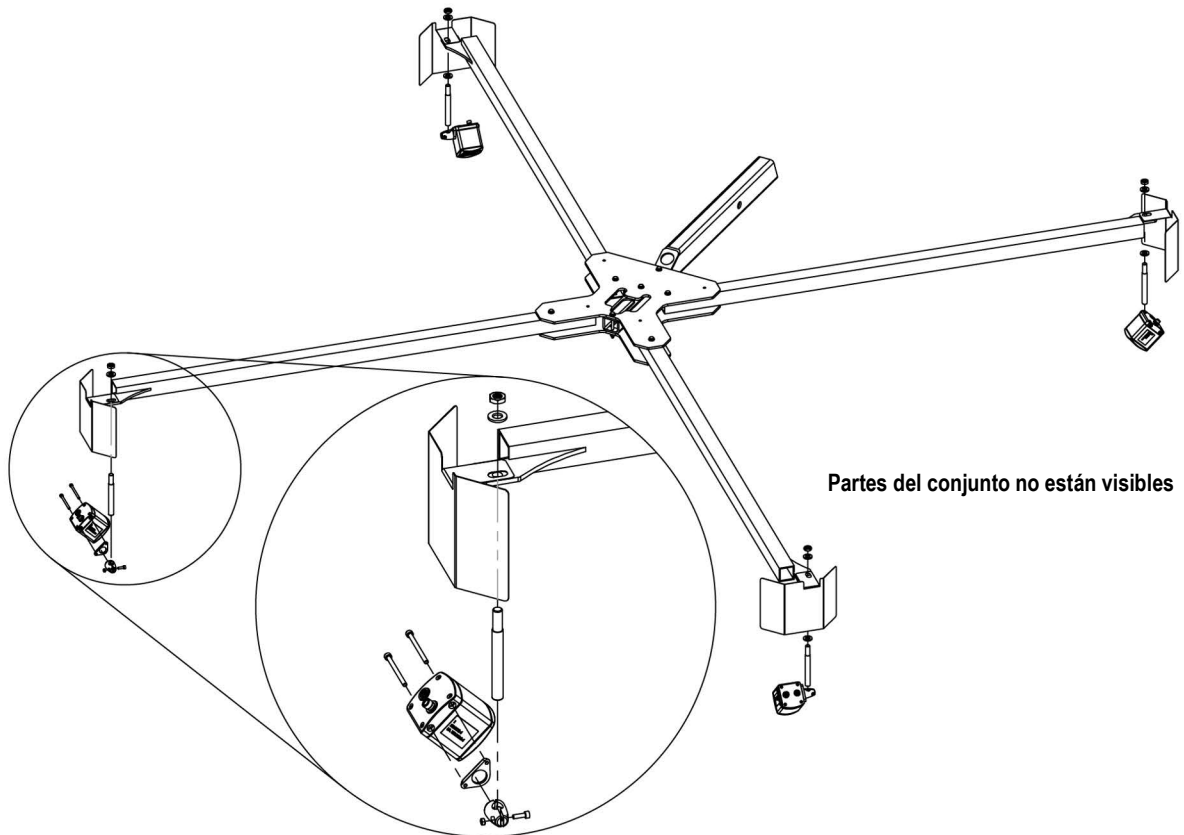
Accesorio para el montaje del sensor remoto IFM
